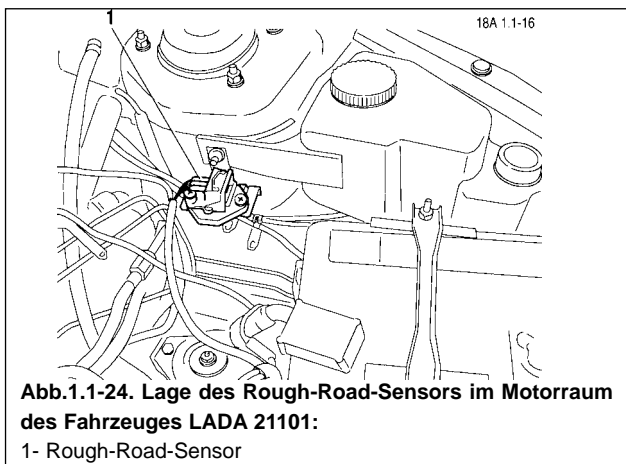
Lage des Rough-Road-Sensors im Motorraum des Fahrzeuges LADA 21101:
